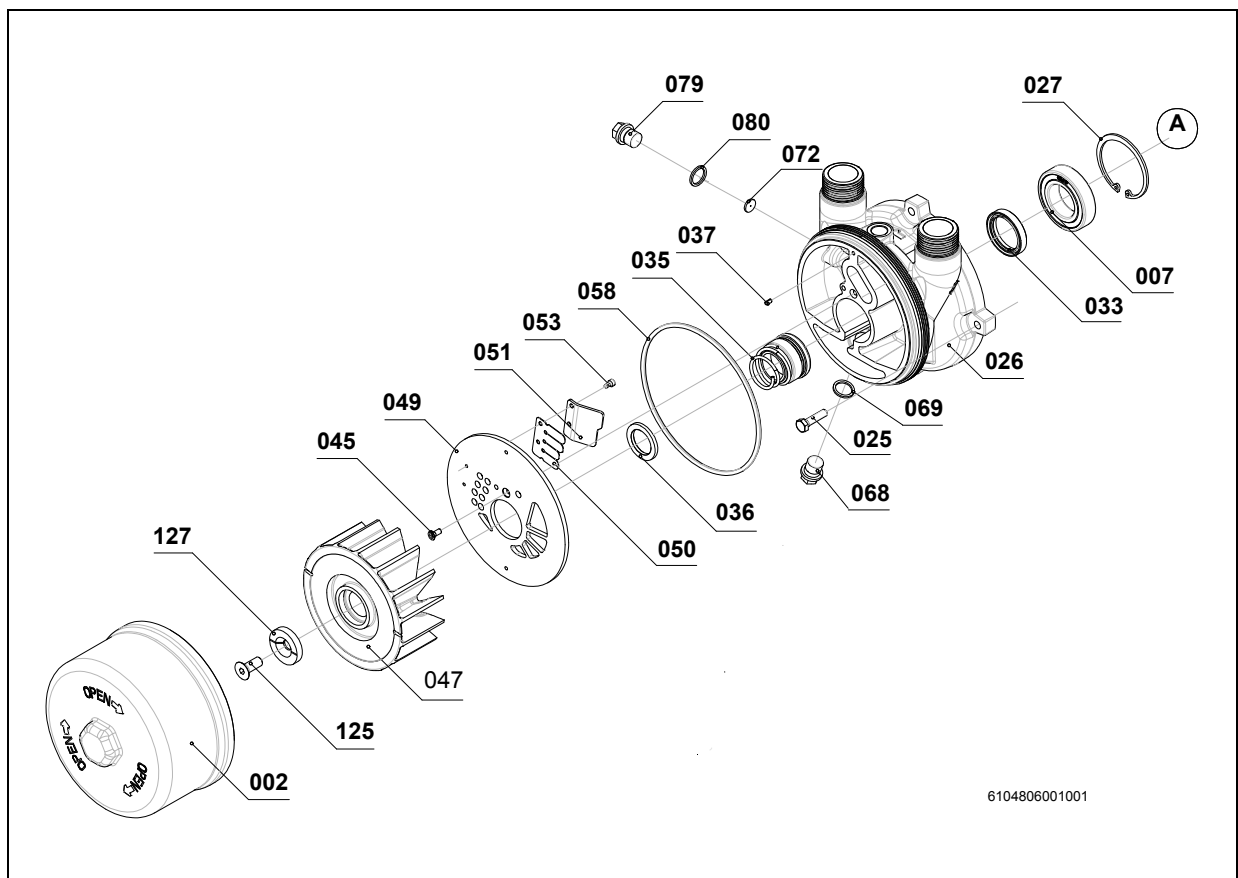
Disegno esploso: componente pompa per vuoto / compressore
